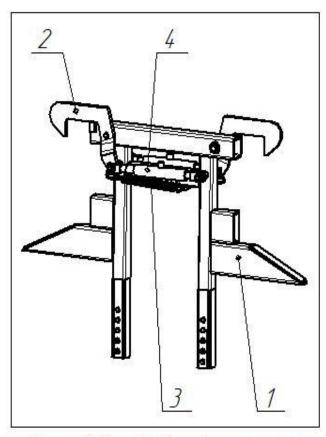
Устройство предохранительное 1 – Рама; 2 – Рычаг; 3 – Пружина; 4 – Гидроцилиндр.
